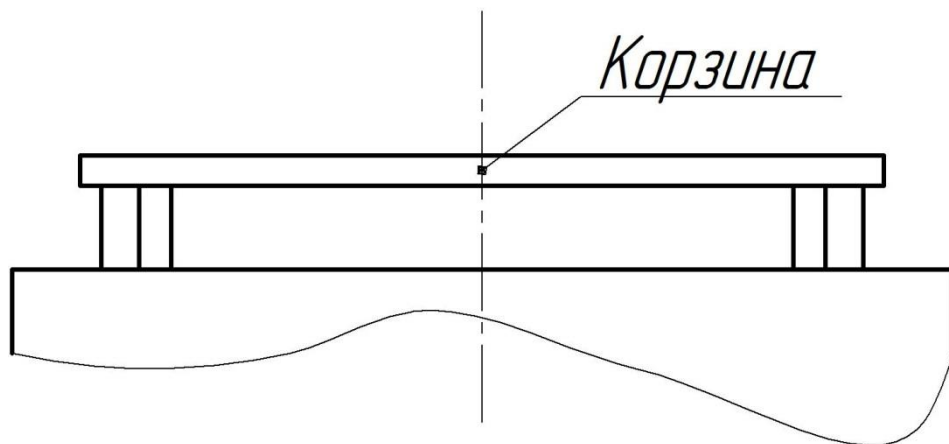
Схема позиции I «загрузка» четырехпозиционного роторного сборочного автомата 9
